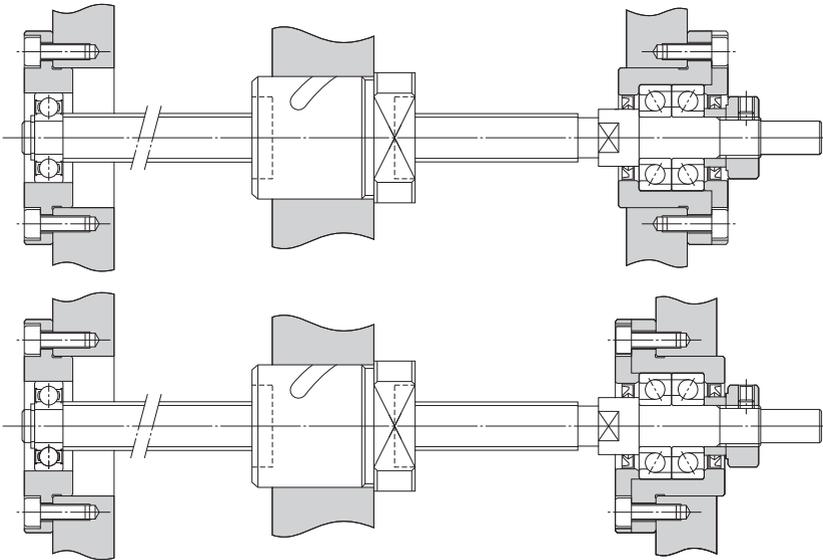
Пример установки концевой подшипниковой опоры круглого типа
